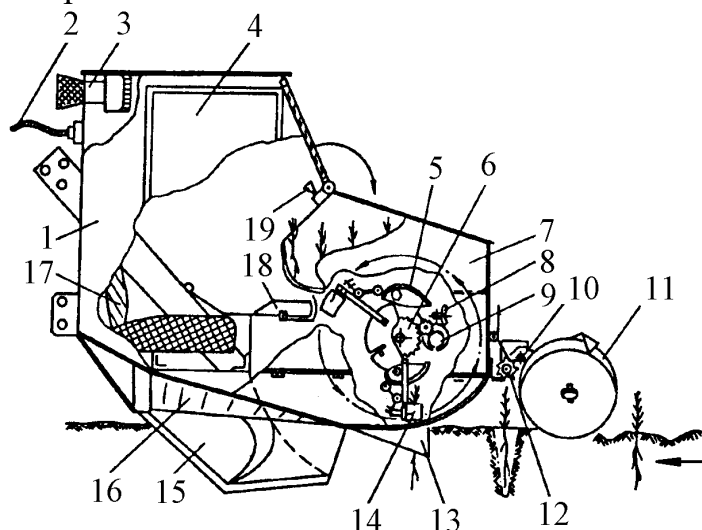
Схема лесопосадочной машины ЛМД-21: 1 – рама; 2 – электропривод; 3 – вентилятор с фильтром; 4 – кабина; 5 – лекало раскрывателя захватов; 6 – зубчатое колесо вала посадочного аппарата; 7 – бункер для посадочного материала; 8 – бортовая электросеть; 9 – электродвигатель постоянного тока; 10 – крестовина; 11 – прикатывающие катки; 12 – храпово-пружинный механизм регулирования давления катков на почву; 13 – заделывающие клинья; 14 – лучевой посадочный аппарат; 15 – сошник; 16 – опорная пластина; 17 – сидение сажальщика; 18 – приемный столик для сеянцев; 19 – панель управления электроприводом
